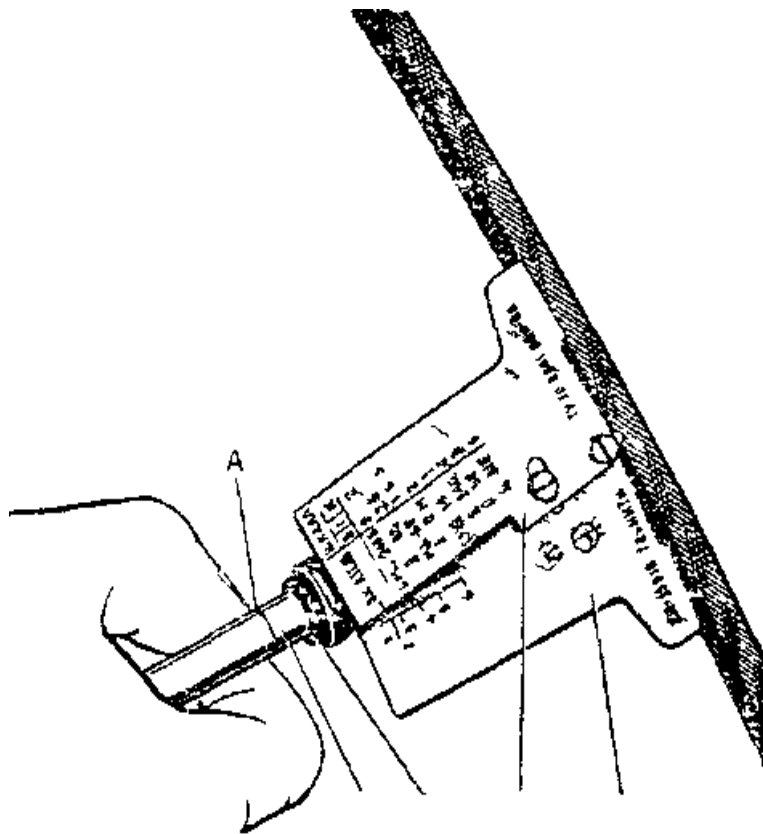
Прибор КИ-13918: 1 – шток; 2 – кольцо; 3,4 – секторы; А – контрольная риска
